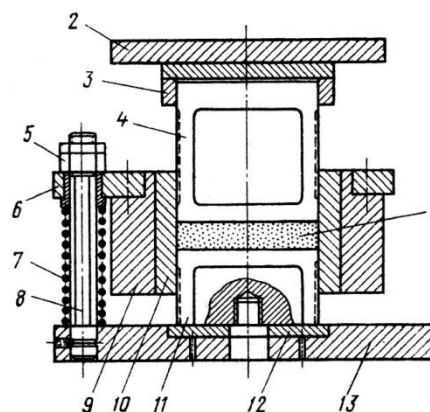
Пресс-форма с «плавающей» матрицей: 1 – пресс-порошок; 2 – верхняя плита; 3 – пуансонодержатель; 4 – верхний пуансон; 5 – регулировочная гайка; 6 – поддерживающая плита; 7 – опорная пружина; 8 – колонка; 9 – обойма; 10 – планки; 11 – нижний пуансон; 12 – опорное кольцо; 13 – опорная плита
